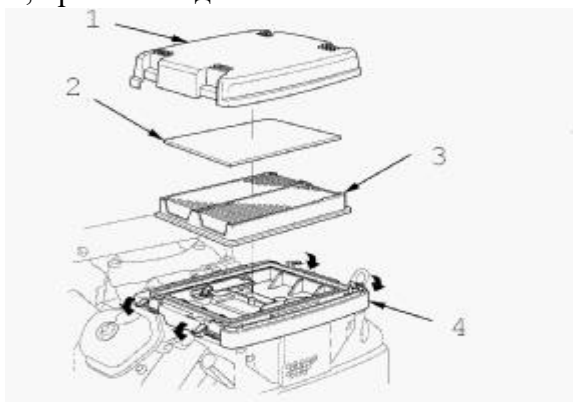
1-крышка; 2- поролоновый элемент; 3- бумажный элемент; 4- корпус
